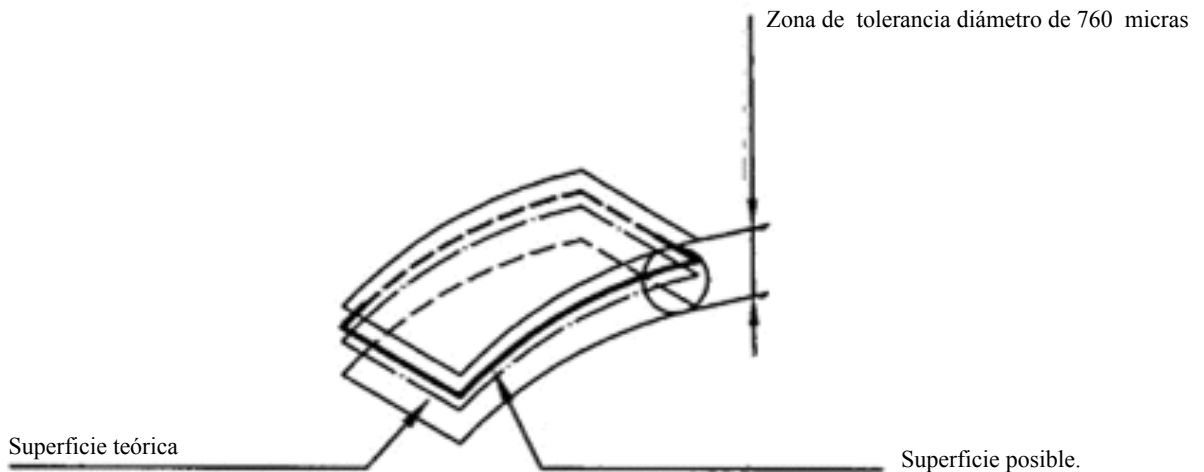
Zona de tolerancia para el perfil de la cara de la pieza.
